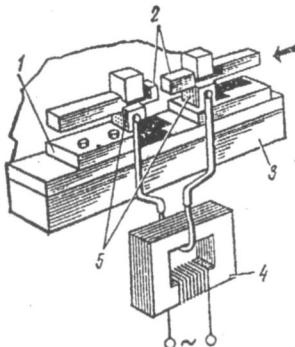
Схема контактнойстыковой сварки: 1 – контактная плита; 2 – свариваемые заготовки; 3 – станина; 4 – трансформатор; 5 – электроды
